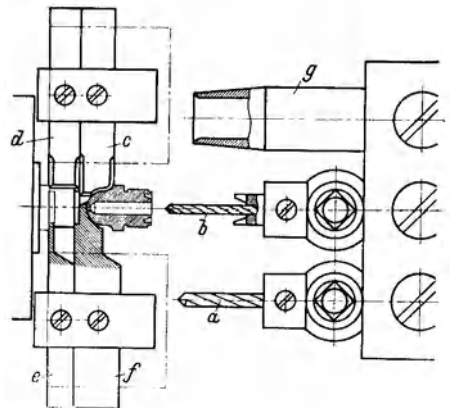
Bearbeitung eines Schmiernippels aus Al-Legierung.
